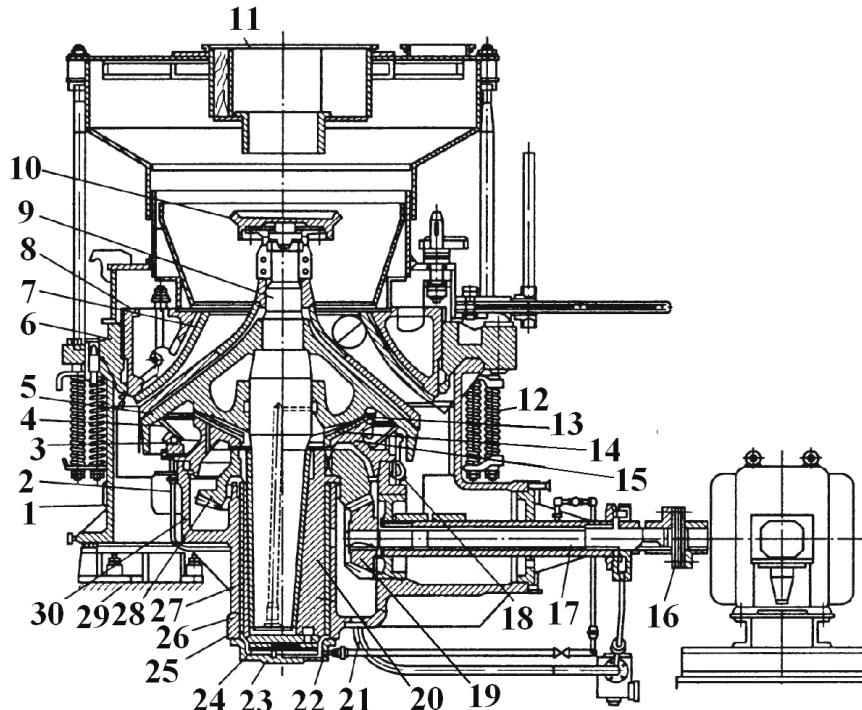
Конусные дробилки для среднего и мелкого дробления типа КСД и КМД
